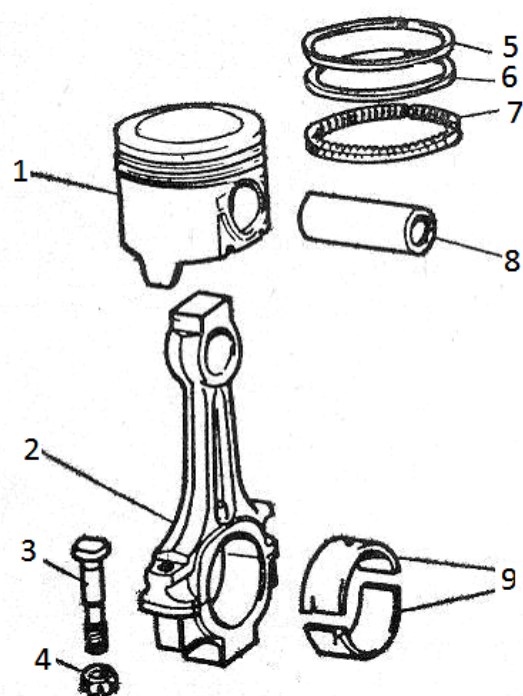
Componente ale mecanismului motor: 1- piston; 2- bielă; 3- șurub; 4- piuliță; 5,6- segmenti etanșare; 7- segment ungere; 8- bolț; 9- cuzineți
